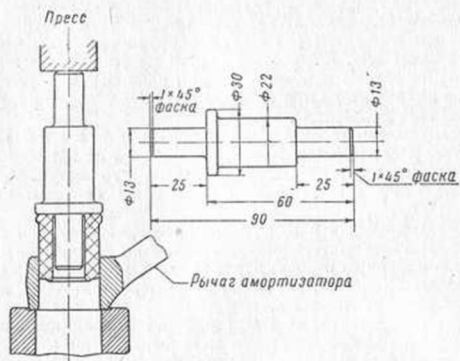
Приспособление и запрессовка резиновой втулки амортизатора.
